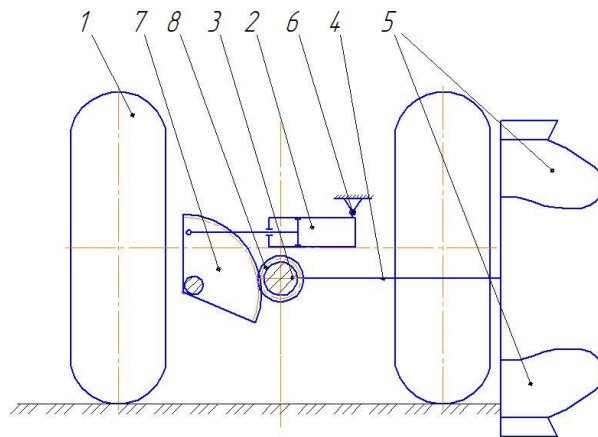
Механізм повороту плуга ПОН-3-30: : 1 – тракторне колесо; 2 – гідроциліндр; 3 – вал основний; 4 – рама кріплення корпусу плуга; 5 – корпус плуга; 6 – тракторна підвіска ; 7 – зубчастий сектор; 8 – шестерня.
